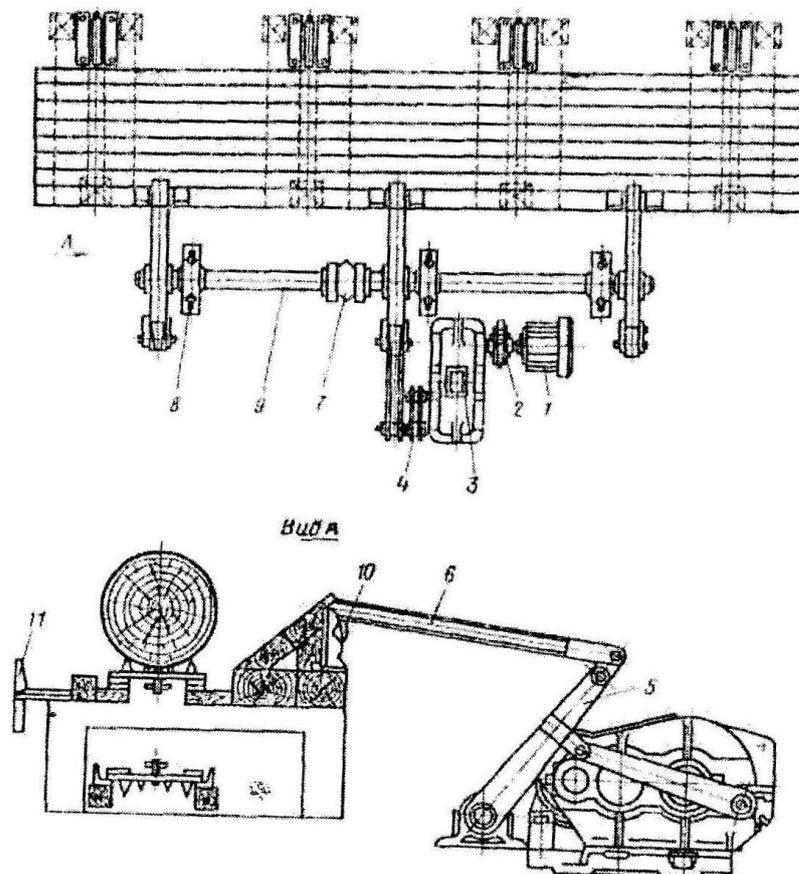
Электромеханический сбрасыватель бревен: 1 – электродвигатель; 2 – муфта и тормоз; 3 – редуктор; 4 – кривошип; 5 – рычаг; 6 – толкатель; 7 – жесткая муфта; 8 – подшипник; 9 – поворотный вал; 10 – ролик; 11 – поворотный рычаг
